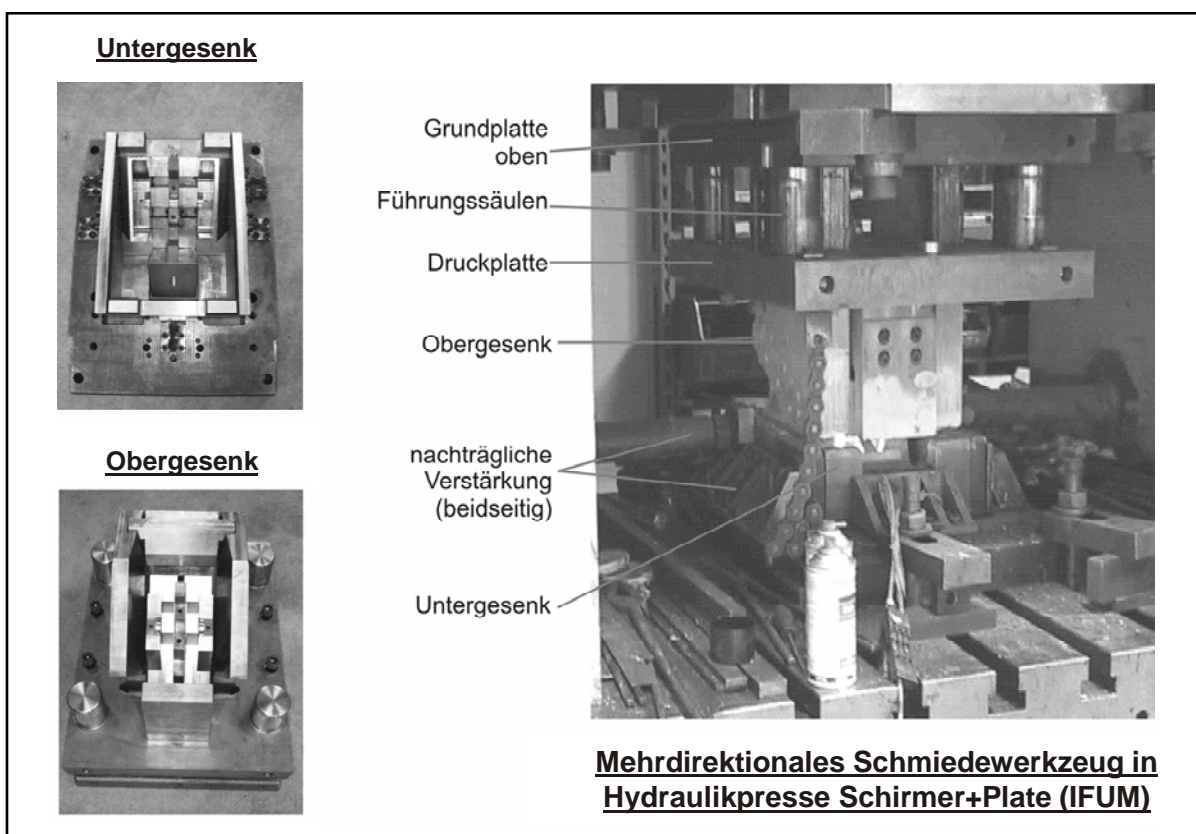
Ansicht des getrennten Ober- und Untergesenks des mehrdirektionalen Schmiedewerkzeugs und des Gesamtwerkzeugs im eingebauten Zustand
